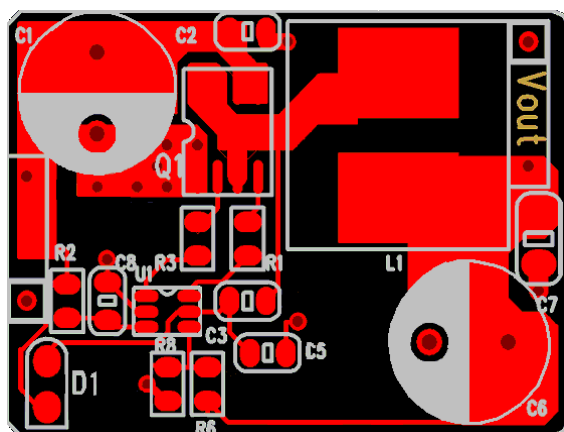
SC2618 评估板 PCB 上层走线 (下层是地)
